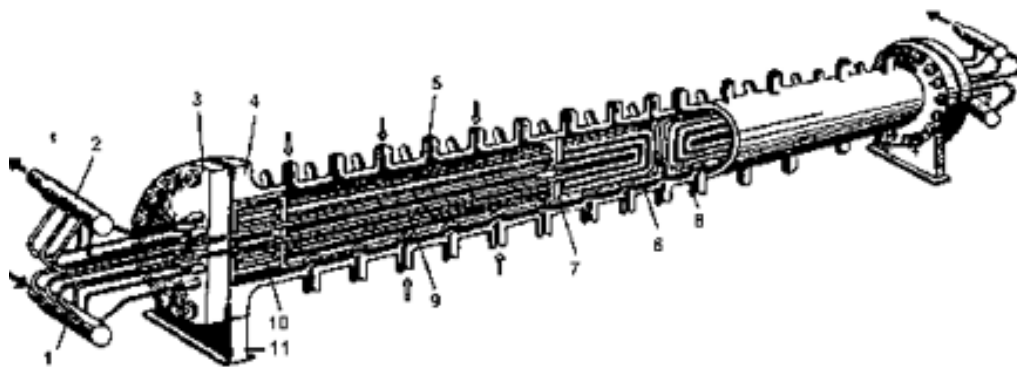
Поверхностный пароохладитель (регулятор перегрева):
